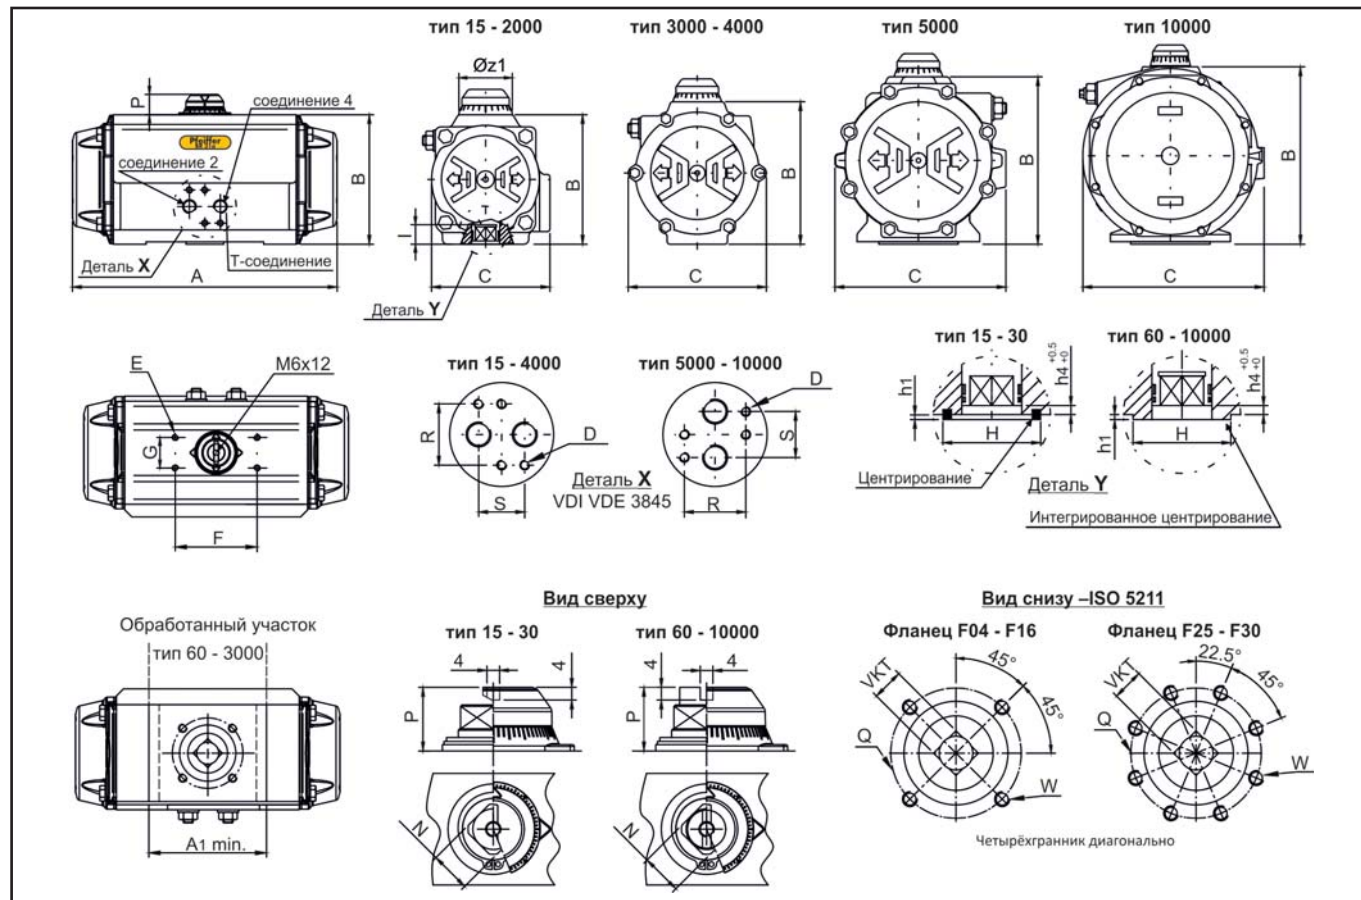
чертеж с размерами поворотного привода серии BR 31a
